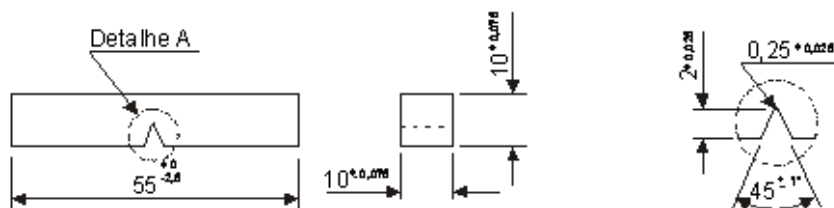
Geometria e dimensões, em milímetros, dos corpos de prova de impacto Charpy tipo A.
